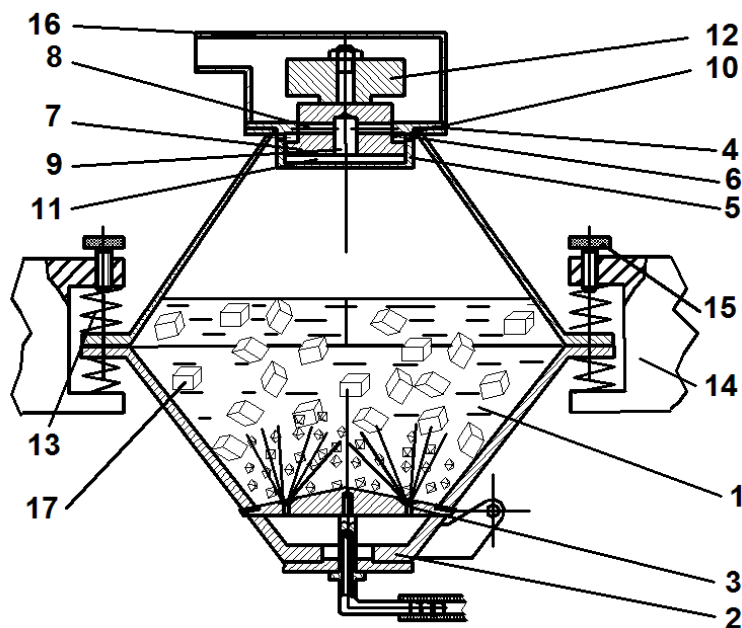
Схема установки для абразивної обробки деталей затопленими струменями
